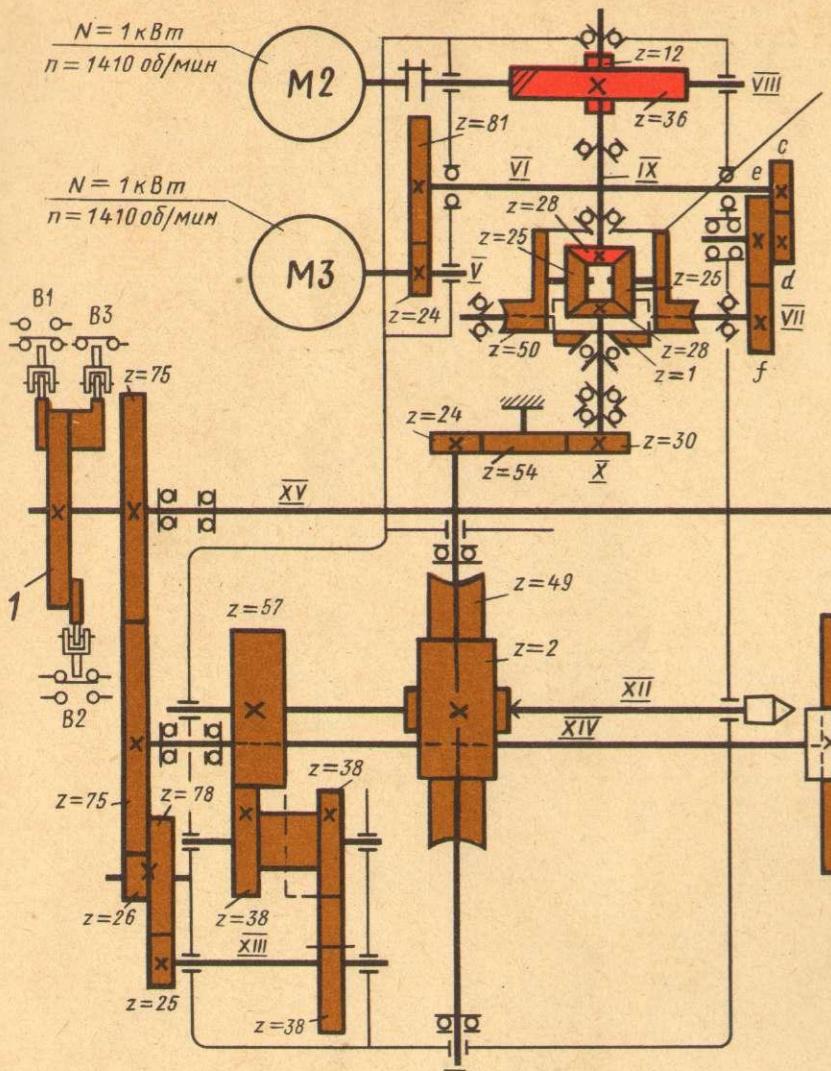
Резьбофрезерный полуавтомат модели 5К63
